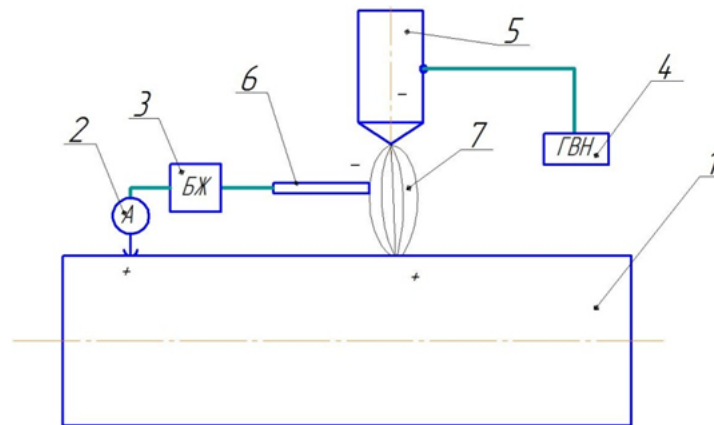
Схема місцевого зміцнення сталевих деталей: 1 – деталь; 2 – електричний струм; 3 – блок живлення; 4 – генератор високої напруги; 5 – електрод коронного розряду; 6 – робочий електрод; 7 – коронний розряд
